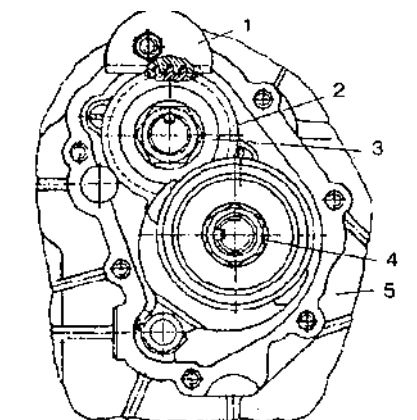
Застопорение пятой передачи коробки передач при отворачивании и заворачивании гаек ведущего и ведомого валов:
